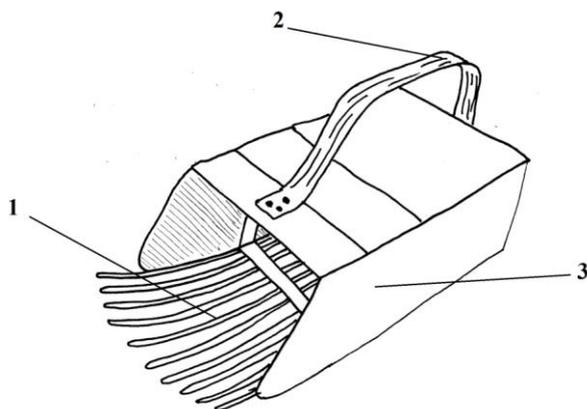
Ручной комбайн для сбора плодов и ягод с кустарничков (черника, брусника, голубика и др.):
